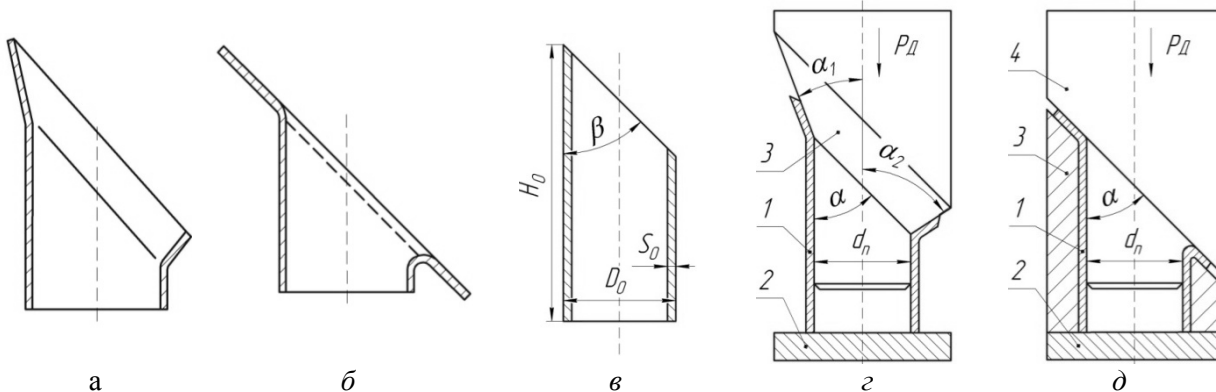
З'єднувальні елементи, вихідна трубчаста заготовка та схеми отримання з'єднувальних елементів: а і б – з'єднувальні елементи, в – вихідна трубчаста заготовка, г – кутова роздача трубчастої заготовки, д – осаджування фланцю
